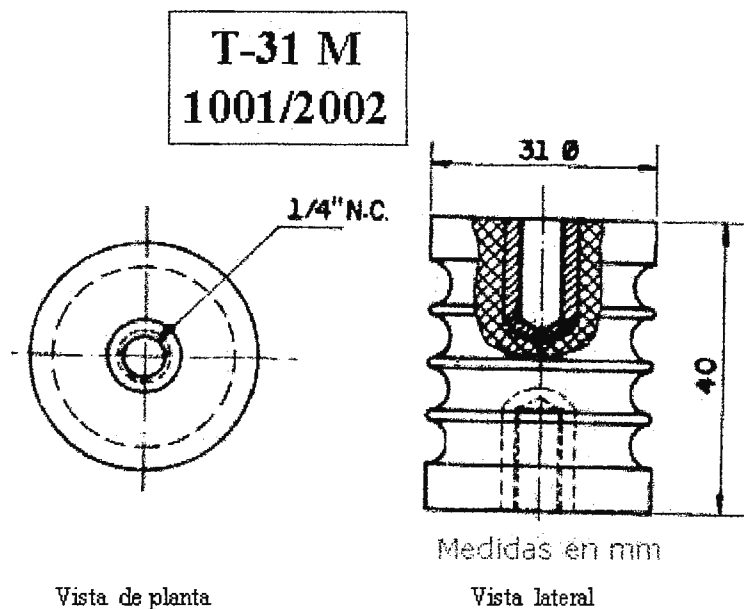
Aislador T-31 para montaje de barras de hasta 30x10mm.
